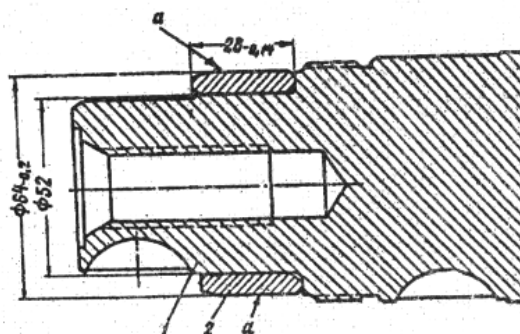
Установка ремонтной втулки под переднюю манжету коленчатого вала: 1 – коленчатый вал; 2 – ремонтная втулка; а – поверхность для полирования
